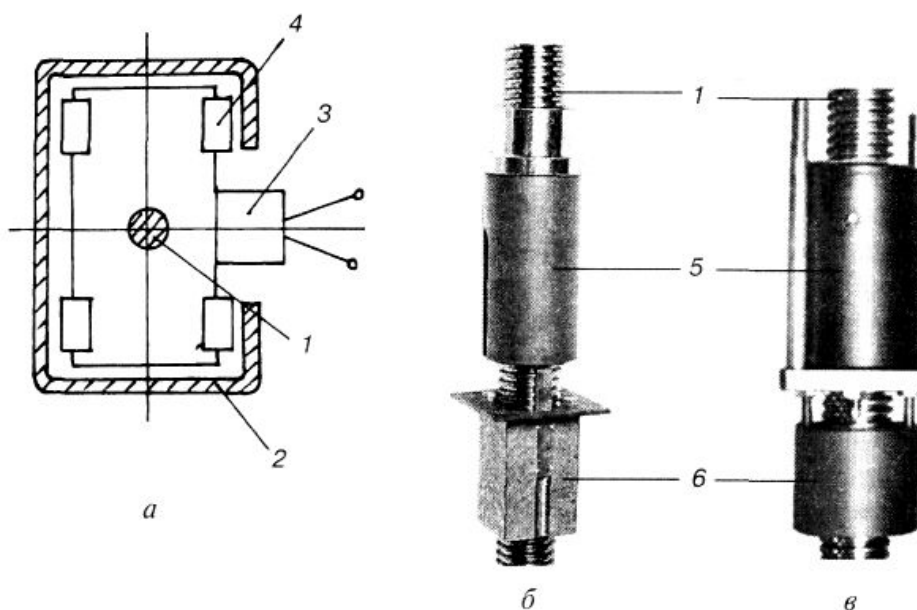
Компоновка каретки в стойке с блоком рабочей и страховочной гаек: а — схема расположения каретки в поперечном сечении стойки; б — блок рабочей и страховочной гаек подъемника ОМА 500; в — то же — подъемника ПС 3 (Россия); 1 — грузовой винт; 2 — стойка; 3 — каретка; 4 — направляющие ролики; 5 — грузовая гайка; 6 — страховочная гайка
